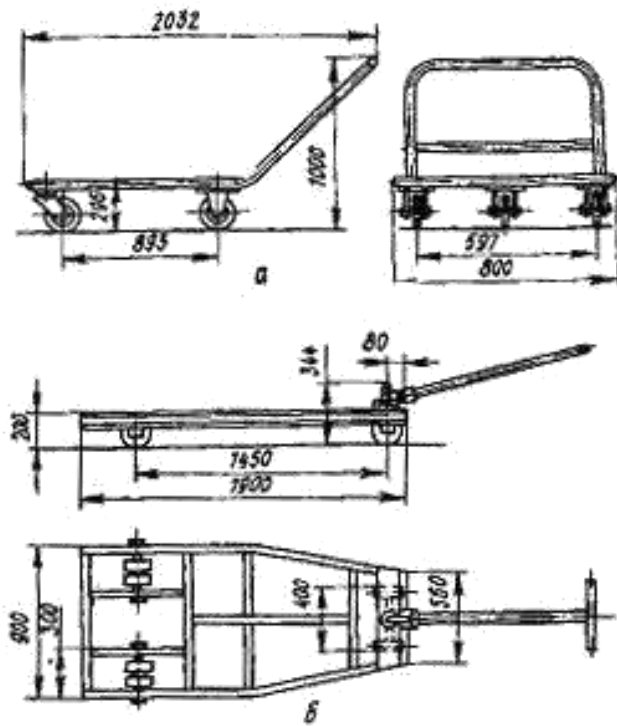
Тележки для перевозки грузов и монтажных заготовок
